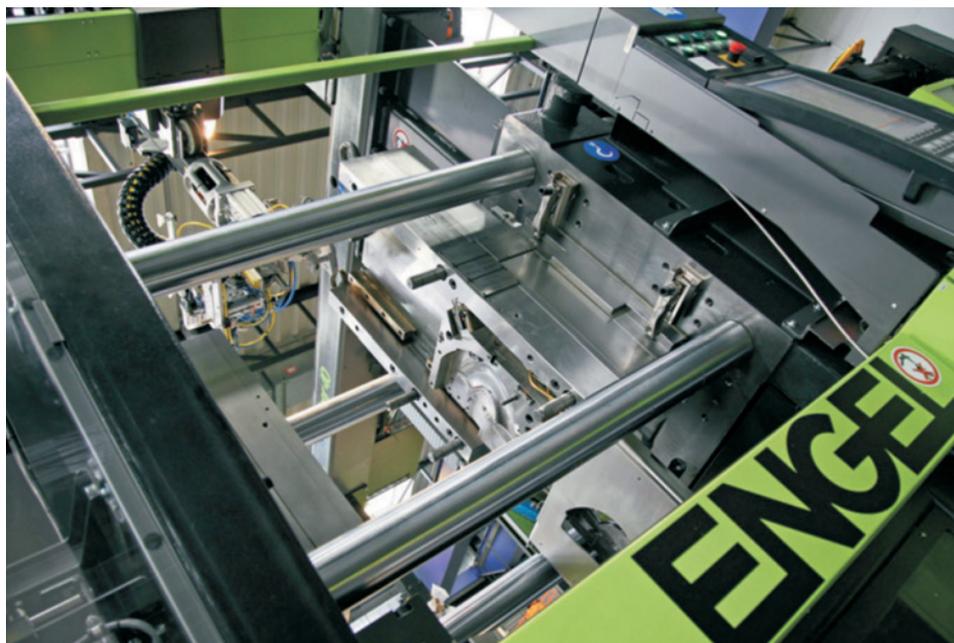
Schiebetischwerkzeug, befestigt auf der festen Schließenseite [Bildquelle: Engel Austria GmbH]
